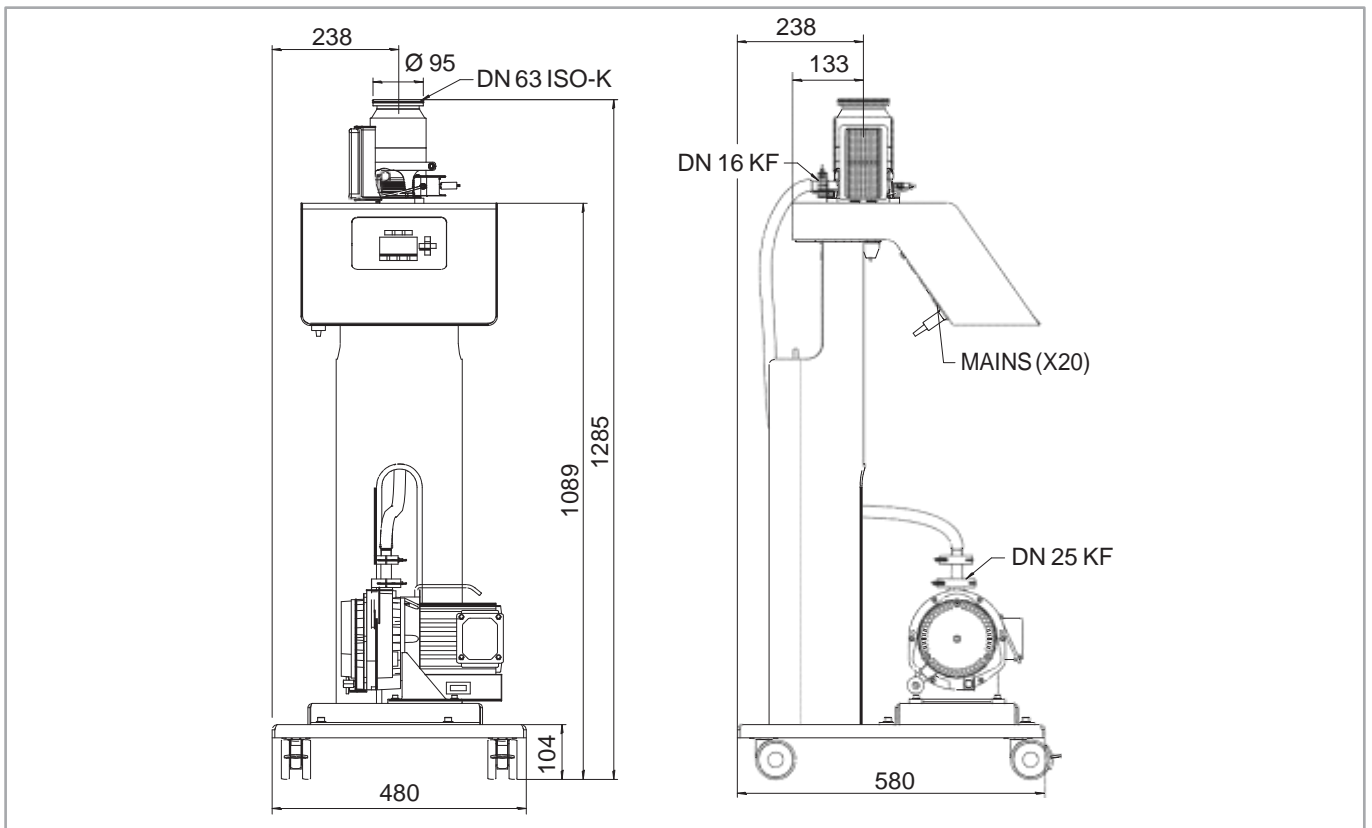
Габаритные размеры TURBOLAB 90 Cart, размеры в мм
